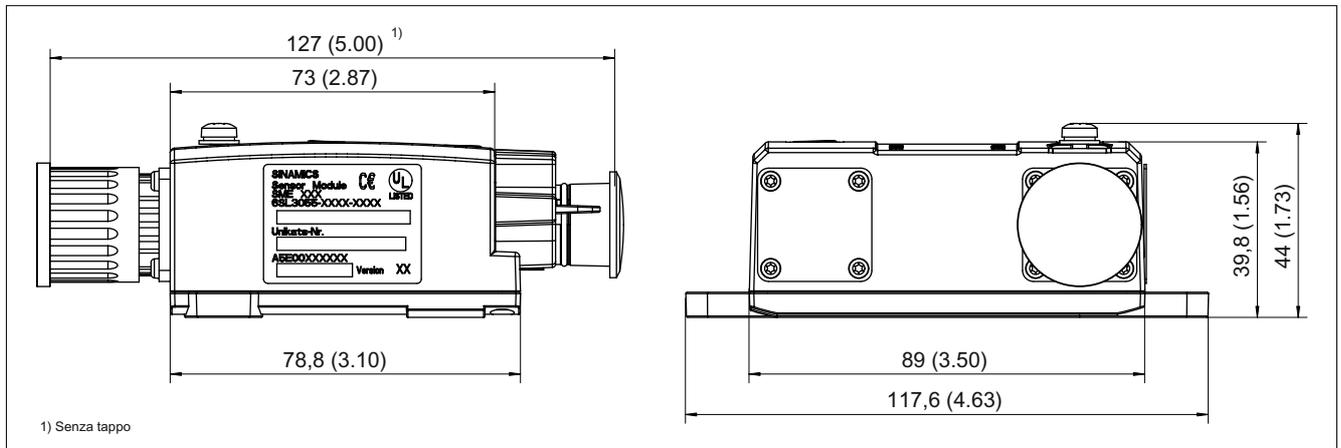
Disegno quotato Sensor Module External SME125, tutte le misure in mm e (inch), N. di ordinazione 6SL3055-0AA00-5KA0
